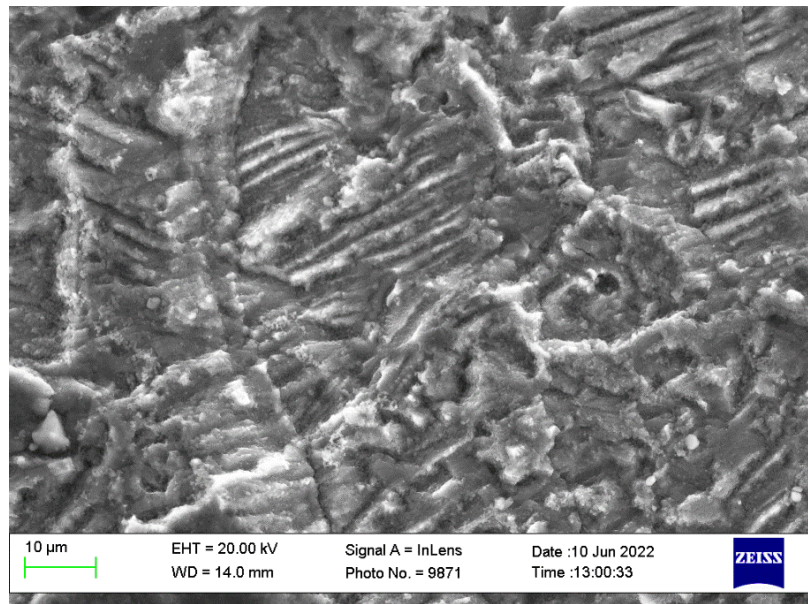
Микрорельеф поверхности излома вблизи очага разрушения.
